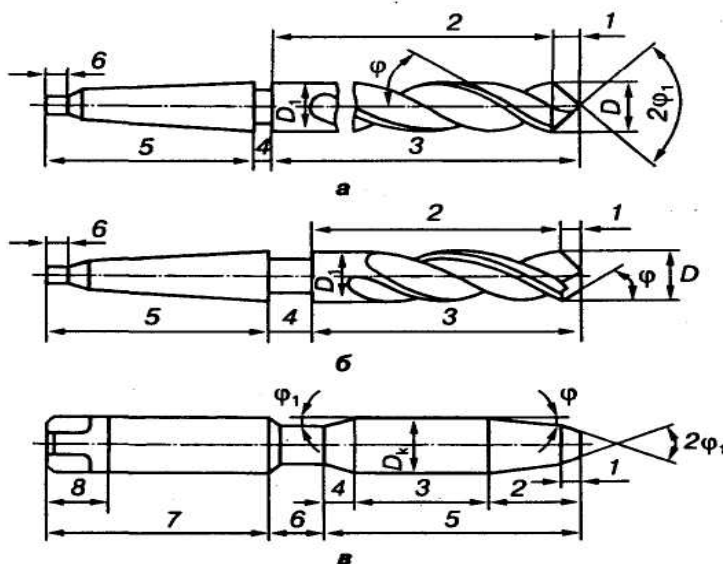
Основні частини та конструкції свердлильних інструментів:
